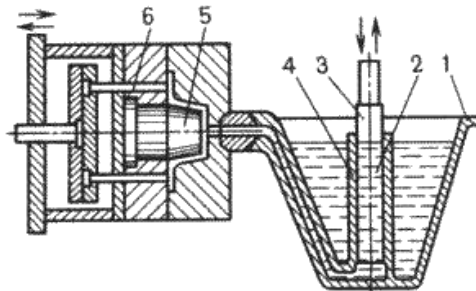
Схема виготовлення виливок на машинах з гарячою камерою пресування.
